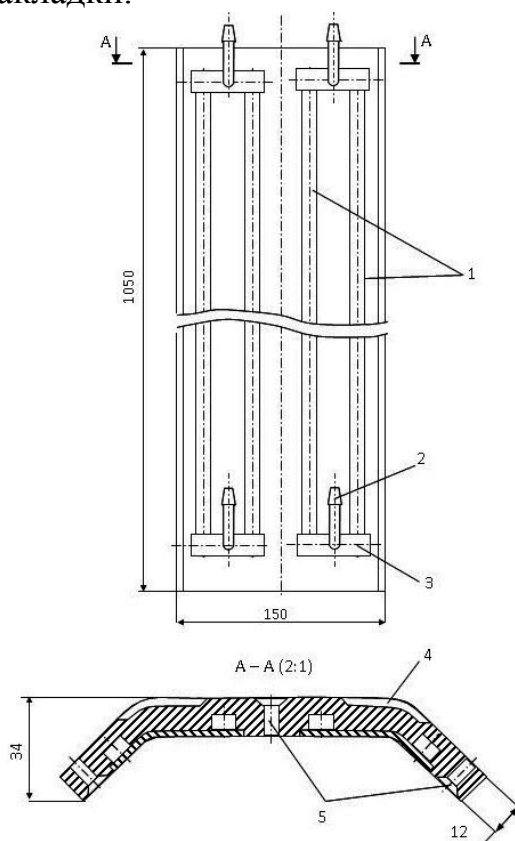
Конструкция медной водоохлаждаемой накладки для формирования обратной стороны электрошлакового шва: 1 – каналы водяного охлаждения; 2 – штуцер; 3 – коллектор; 4 – противоположная канавка; 5 – крепёжные отверстия.
